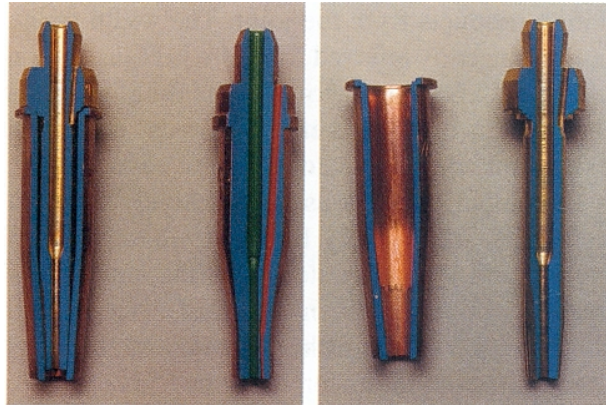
Derecha: boquilla de una pieza. Izquierda: boquilla de dos piezas
